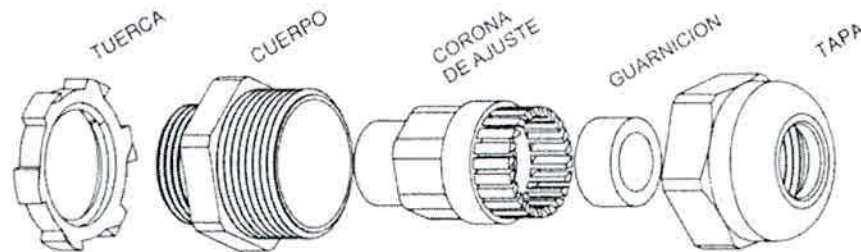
, DESPIECE DE PRENSA CABLES PLÁSTICO CON AJUSTE DE CORONA DENTADA
